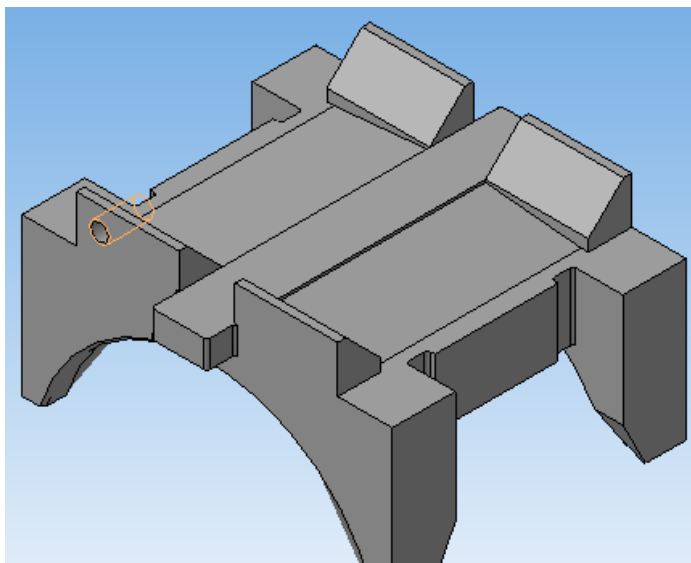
3Д модель "Адаптер подшипникового узла"
